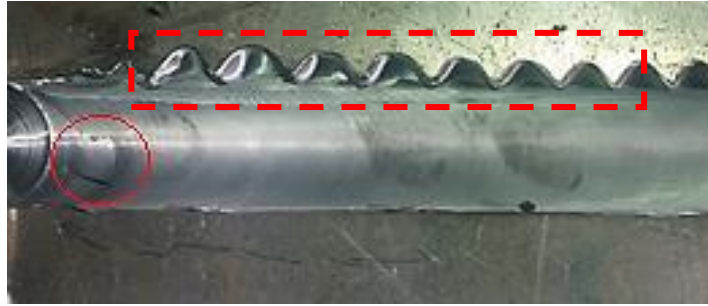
Joints des soudures et fonds des joints pour différents paramètres de soudage.
